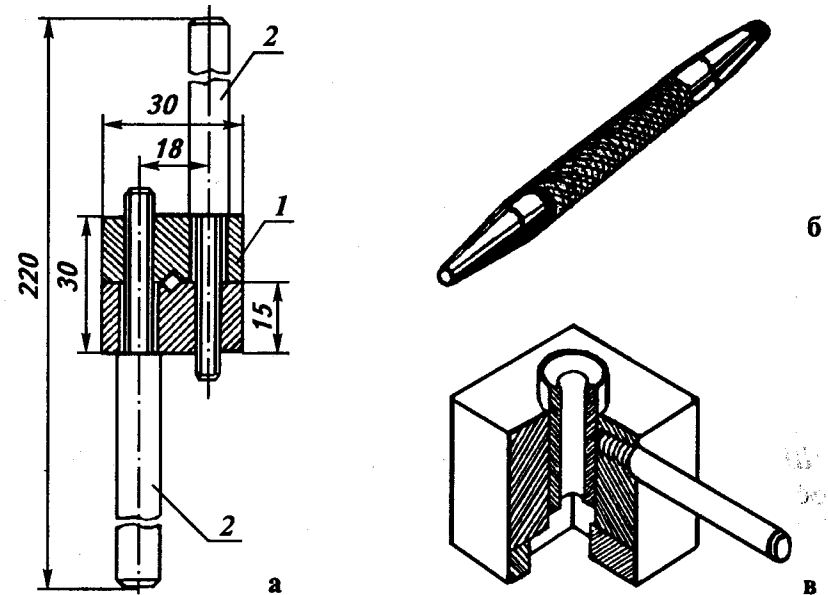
Изделия, выполненные на токарном и фрезерном станках:
